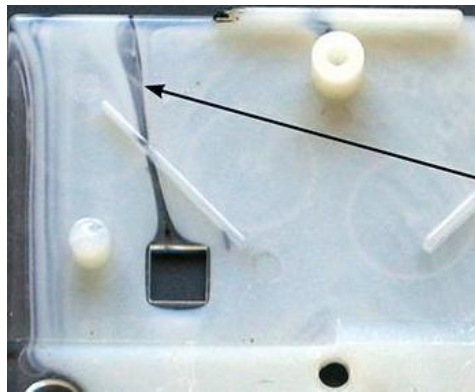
Línea de soldadura muy pronunciada
